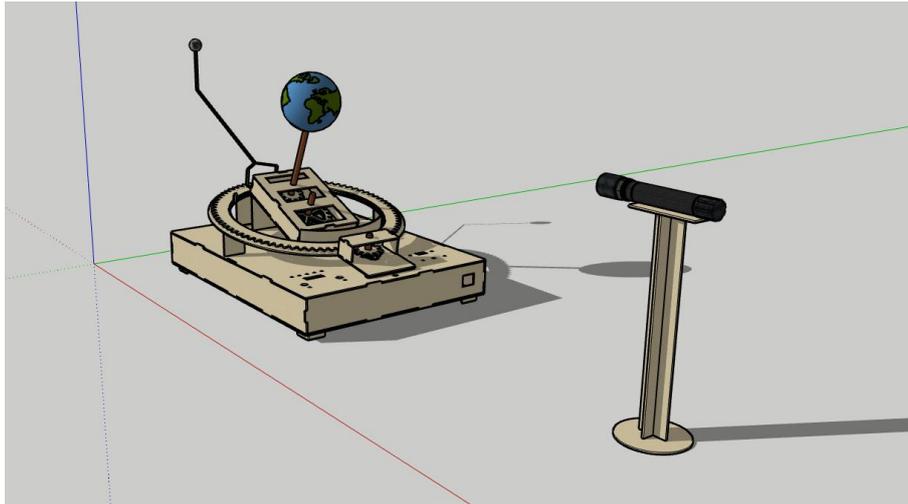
Estrutura completa faltando apenas os componentes eletrônicos.
